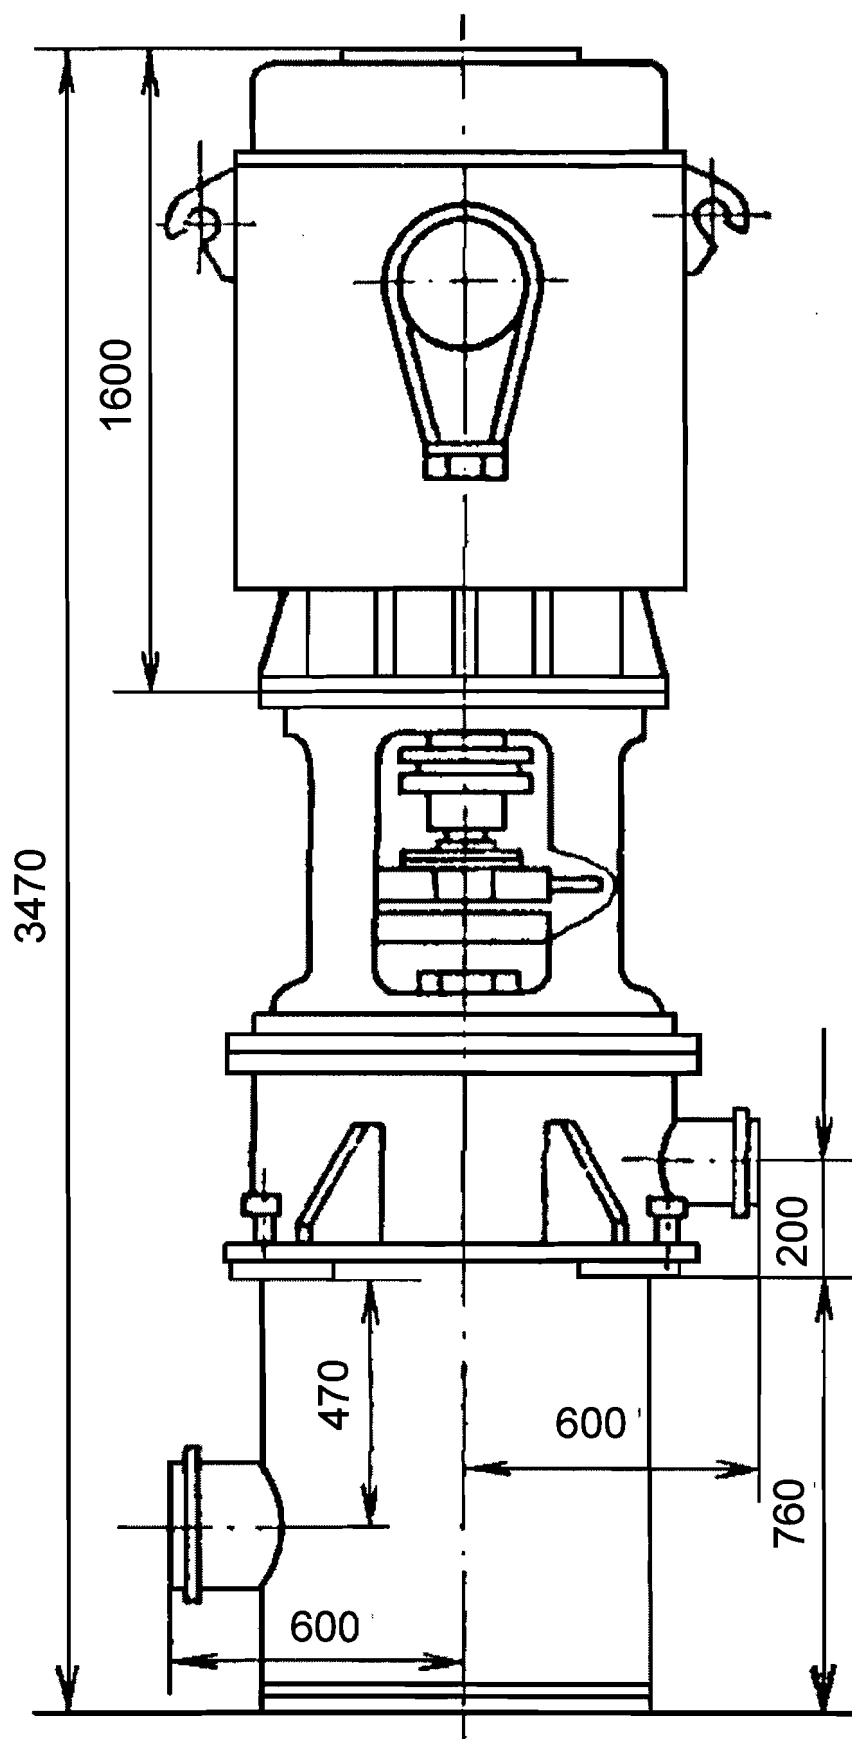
Общий вид насосного агрегата КсВА-360-160
